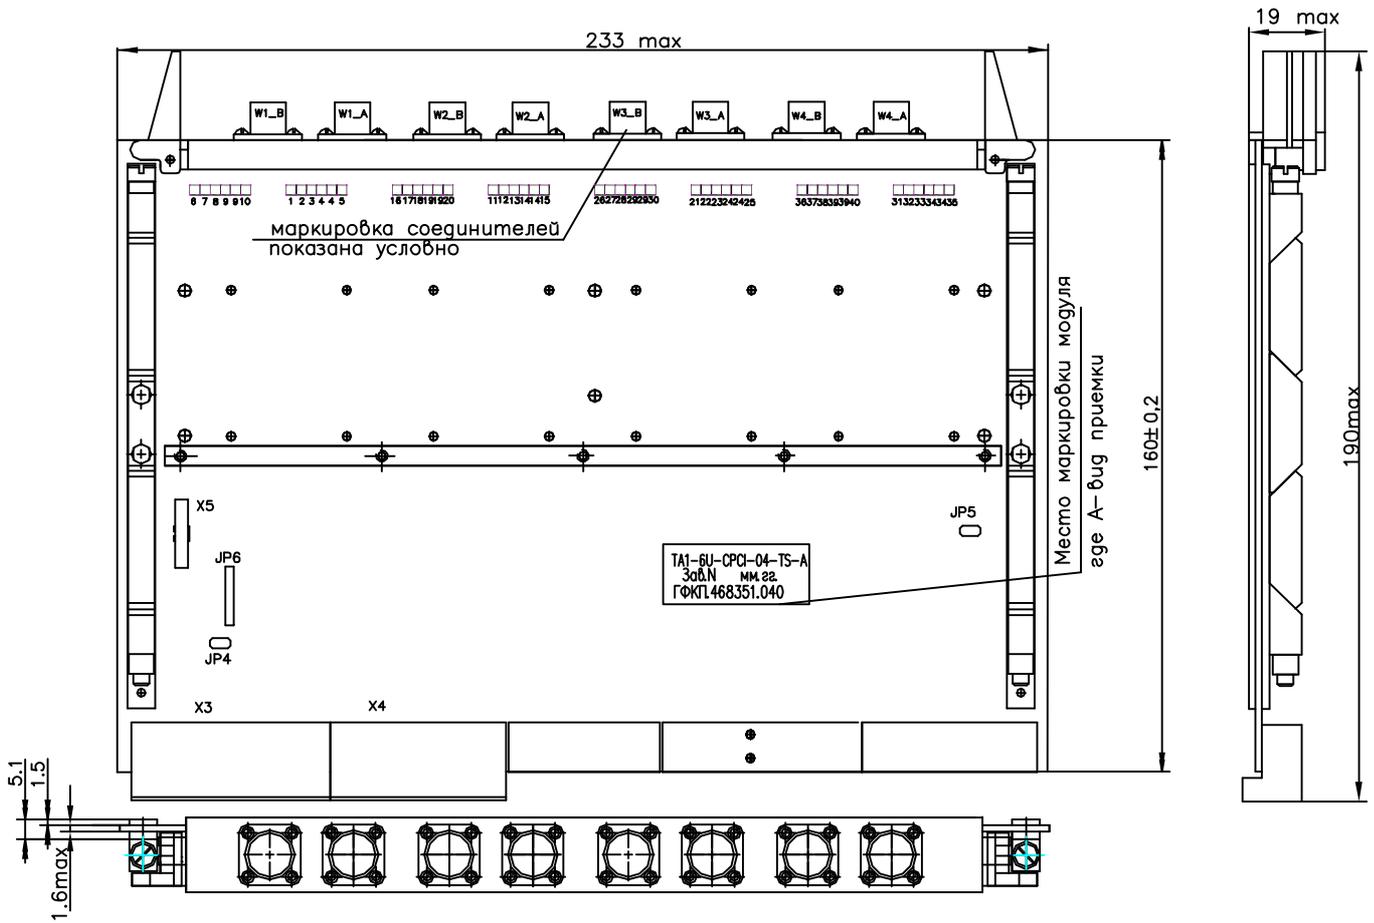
Габаритный чертеж изделия TA1-6U-CPCL-04-TS –A с кондуктивным теплосъемом и выходными разъемами PC7TB
